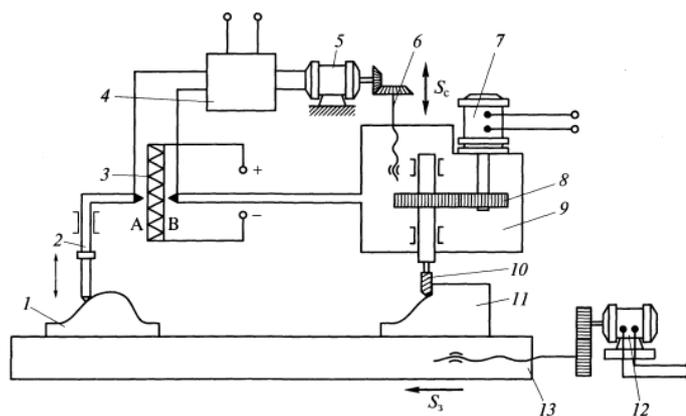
Принципиальная схема следящей системы копировального станка: 1 — копир; 2 — щуп; 3 — сопротивление; 4 — усилитель; 5, 7, 12 — электродвигатели; 6 — ходовой винт; 8 — шестерня; 9 — шпиндельный узел; 10 — фреза; 11 — изделие; 13 — стол
